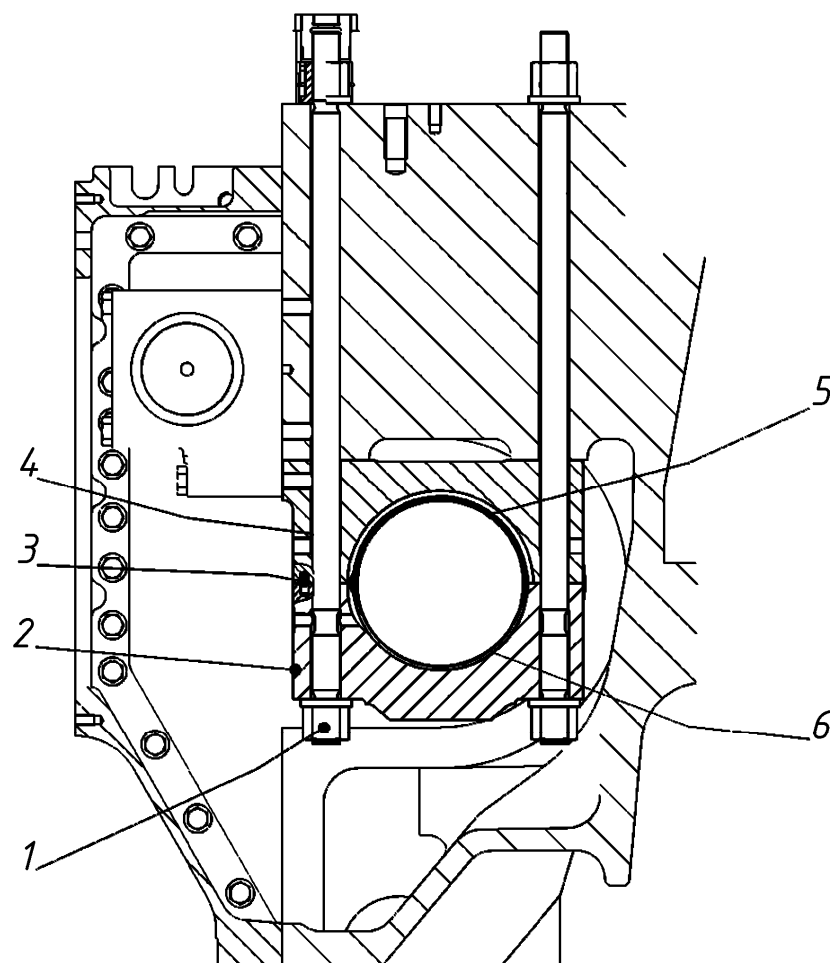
Кріплення розподільного валу дизеля 8L48/60: 1 – гайка кріплення; 2 – нижня кришка корпусу підшипнику; 3 – штифт; 4 – верхня кришка корпусу підшипнику; 5 – верхній вкладиш підшипника ковзання; 6 – нижній вкладиш підшипника ковзання
